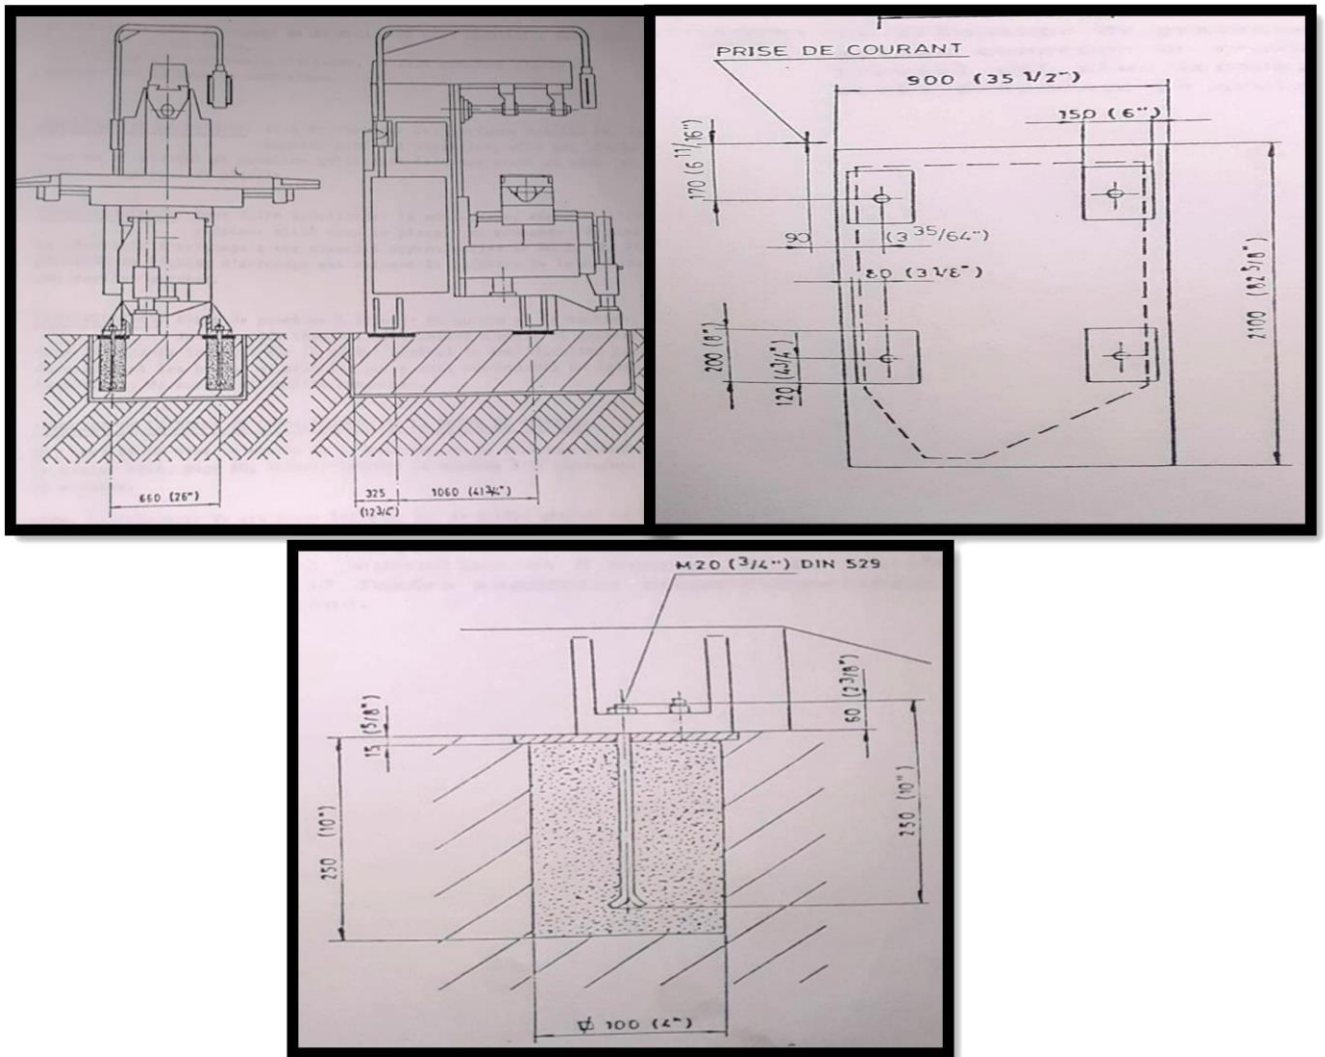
Schémas dimensionnelle de fraiseuse FU-1800 [60].
